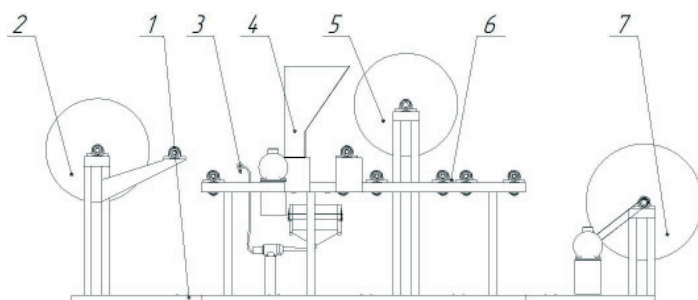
Схема общей компоновки станка: 1 – станина; 2 – разматывающий узел для первого слоя ткани; 3 – механизм подачи связующего вещества; 4 – механизм высева семян; 5 – разматывающий узел для второго слоя ткани; 6 – система сушки; 7 – механизм намотки готовой продукции
